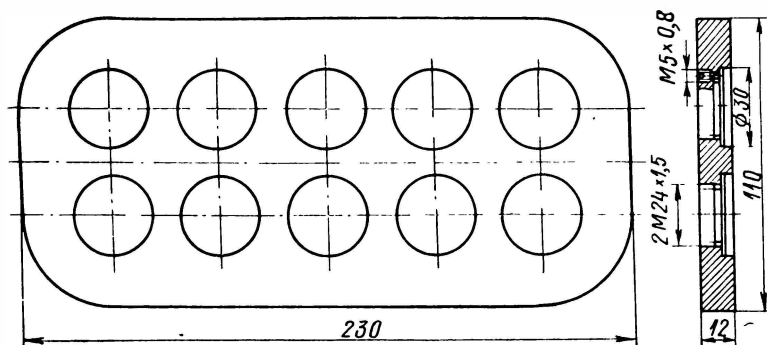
Планка с образцами для установки в камере рабочего колеса
